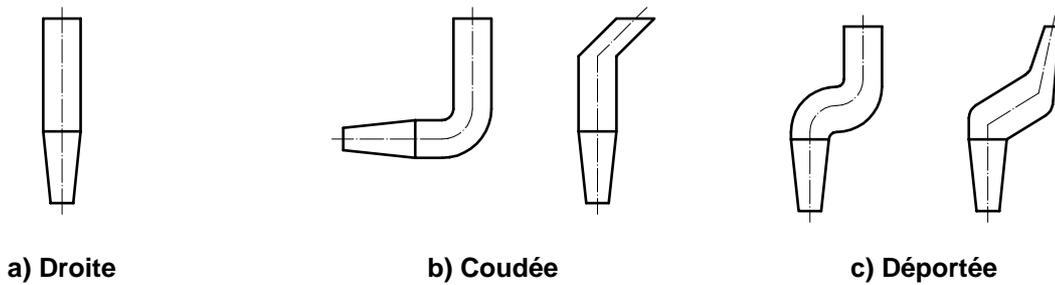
Électrodes de soudage par points avec cône mâle à l'extrémité du montage et extrémité plate
